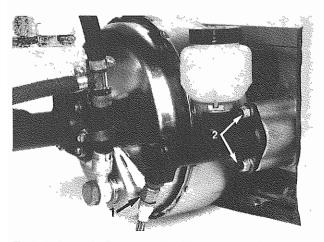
1 - Raccordo di mandata olio - Oil supply connector 2 - Dadi fissaggio pompa primaria - Master cylinder fixing nuts
